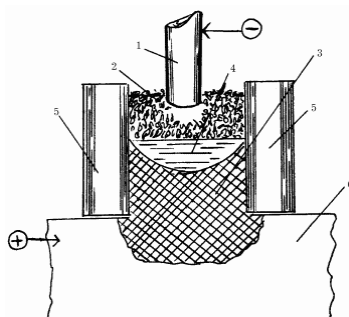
Электрошлаковая сварка: 1 – электрод; 2 – электропроводный шлак; 3 – образуемый шов; 4 – сварочная ванна; 5 – перегородки, формирующие шов; 6 – металл.
